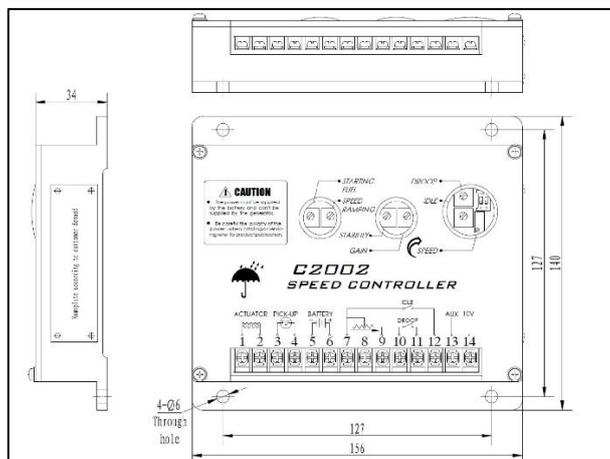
А – Габаритные и присоединительные размеры регулятора скорости С2002
